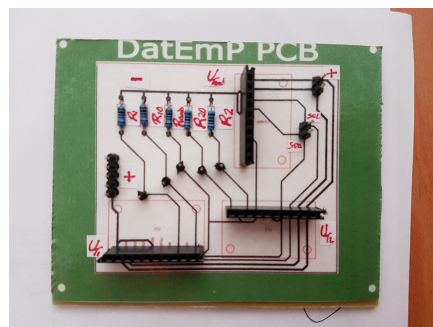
Vista superior de la placa PCB desarrollada con resistencias de  $1\text{ k}\Omega$  soldadas.
